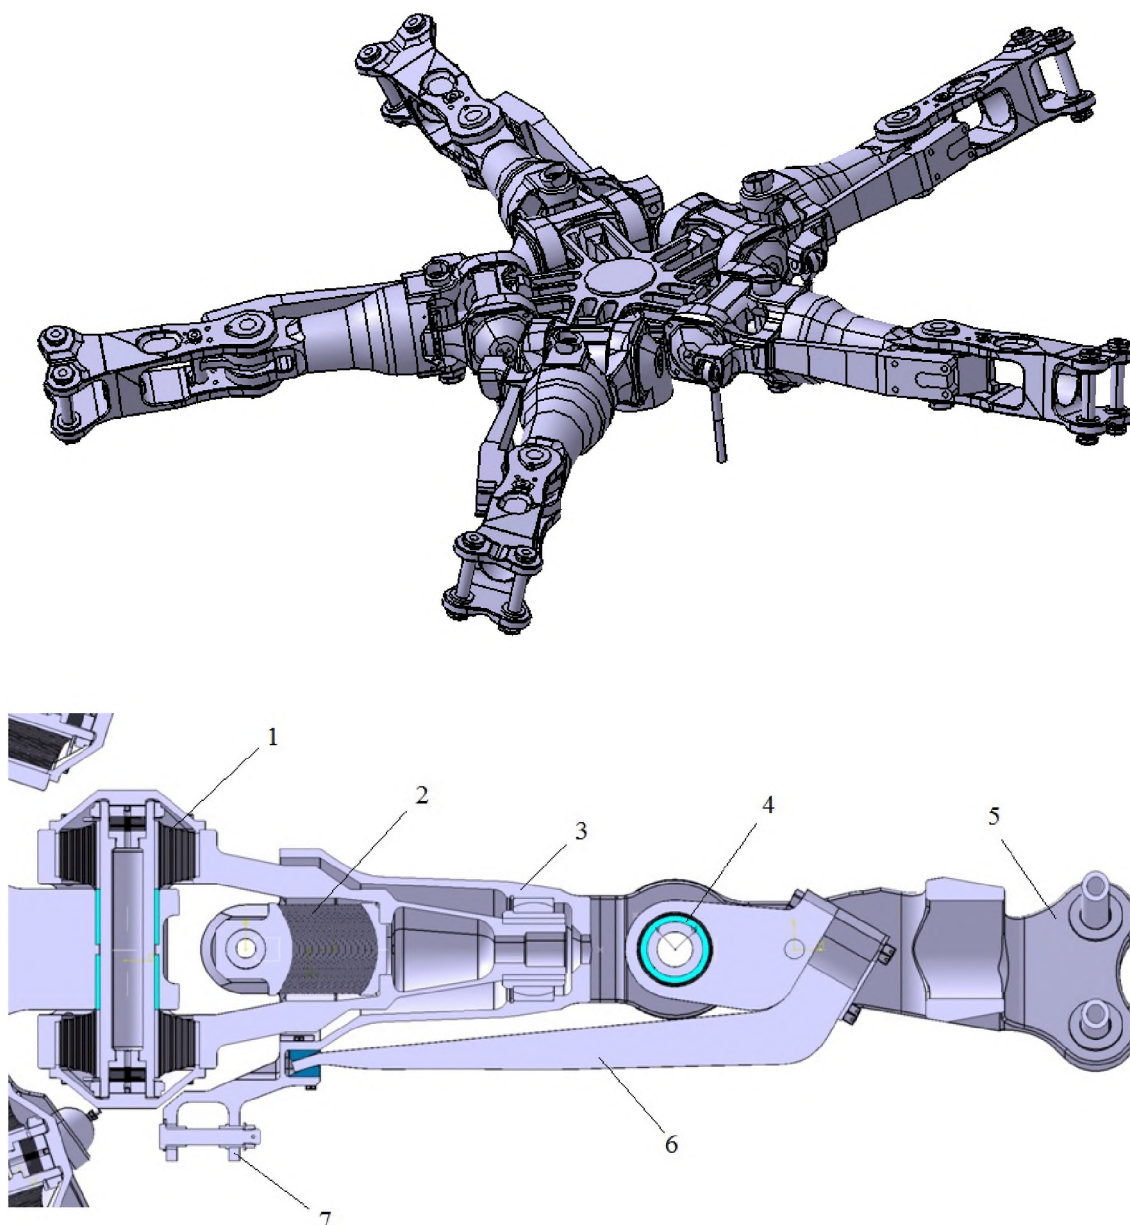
Общий вид и конструкция втулки НВ с эластомерными подшипниками вертолета Ка-62 [24]:
